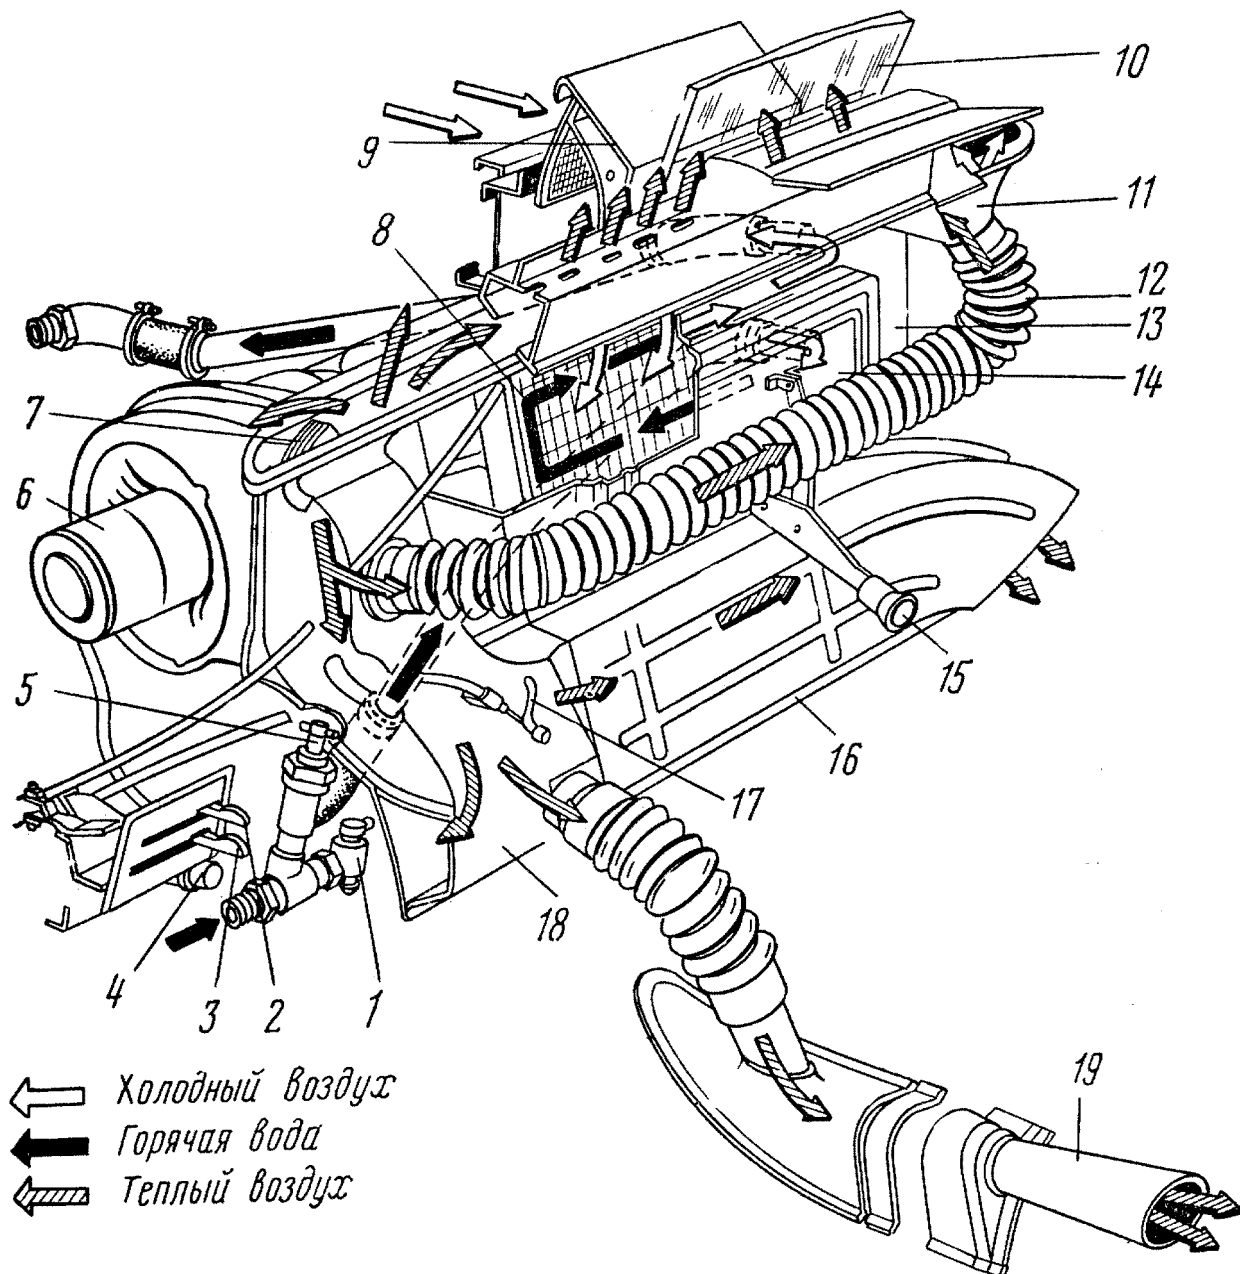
Устройство отопления и вентиляции кузова и обдува ветрового стекла:
